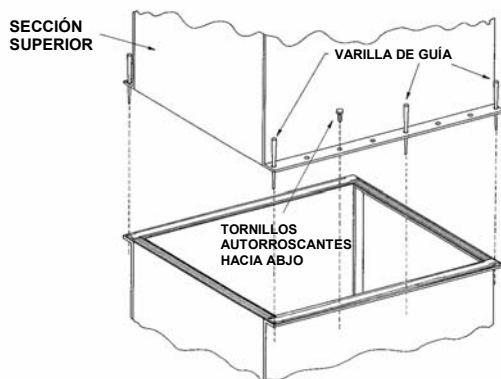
Emparejamiento de la Sección Superior Sobre la Sección de Bandeja
